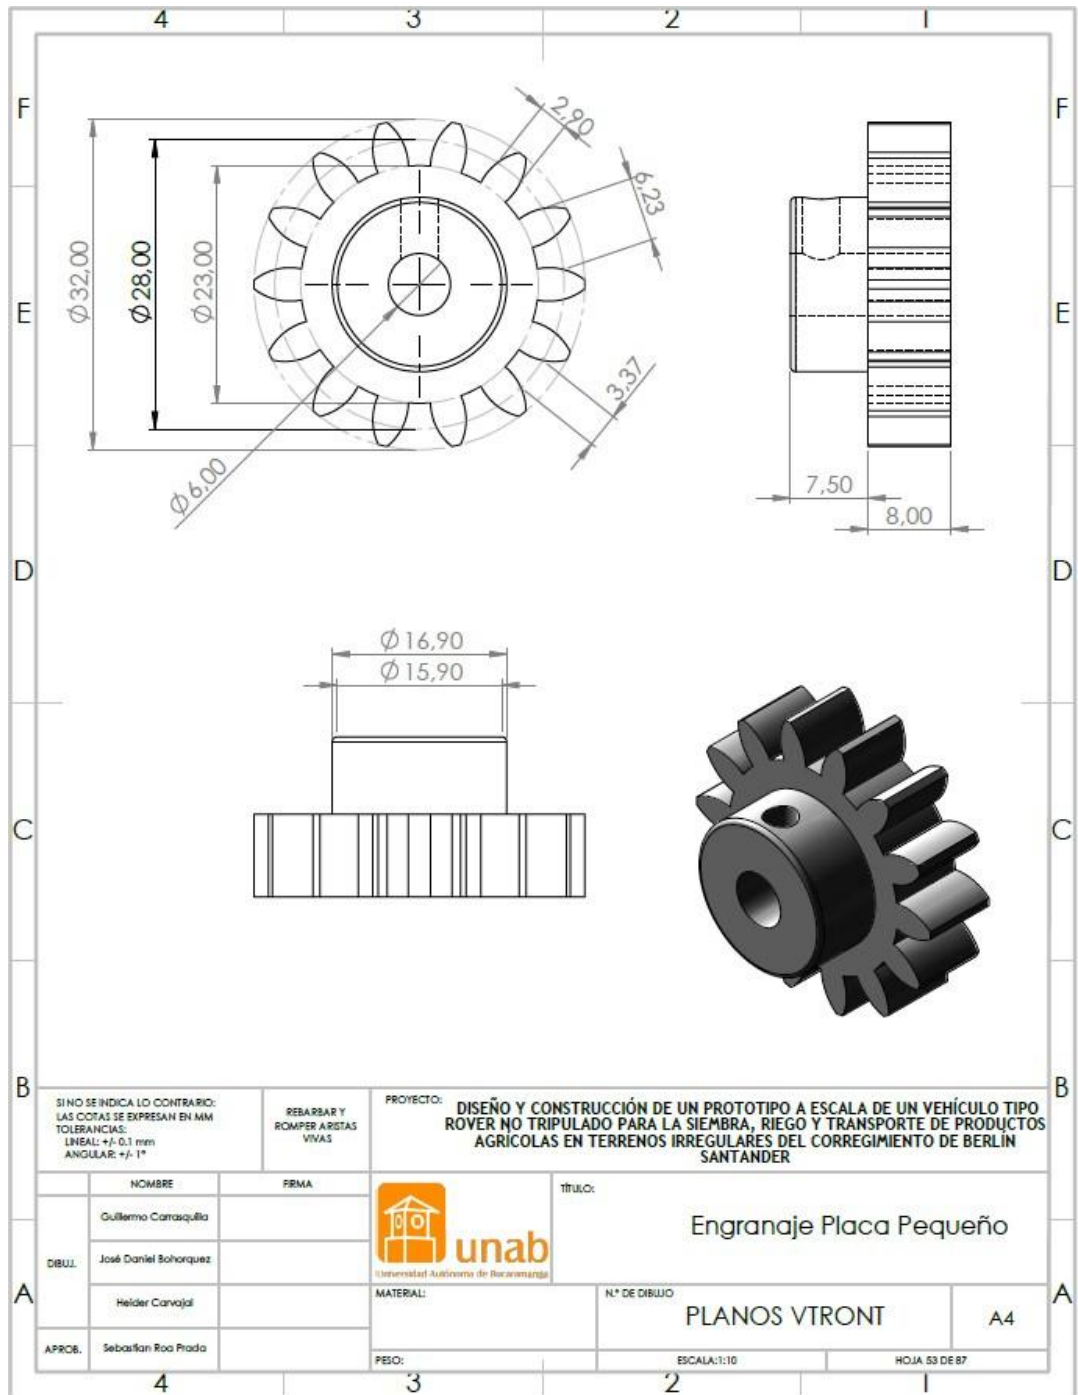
Plano de engranaje del motorreductor de la placa.
